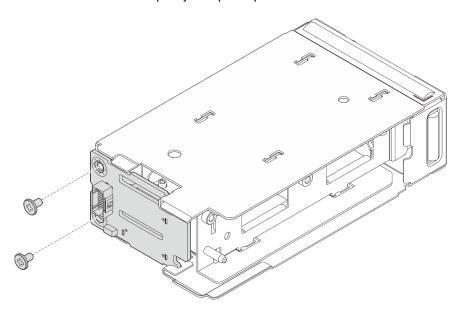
Extracción de la placa posterior de arranque M.2 frontal
